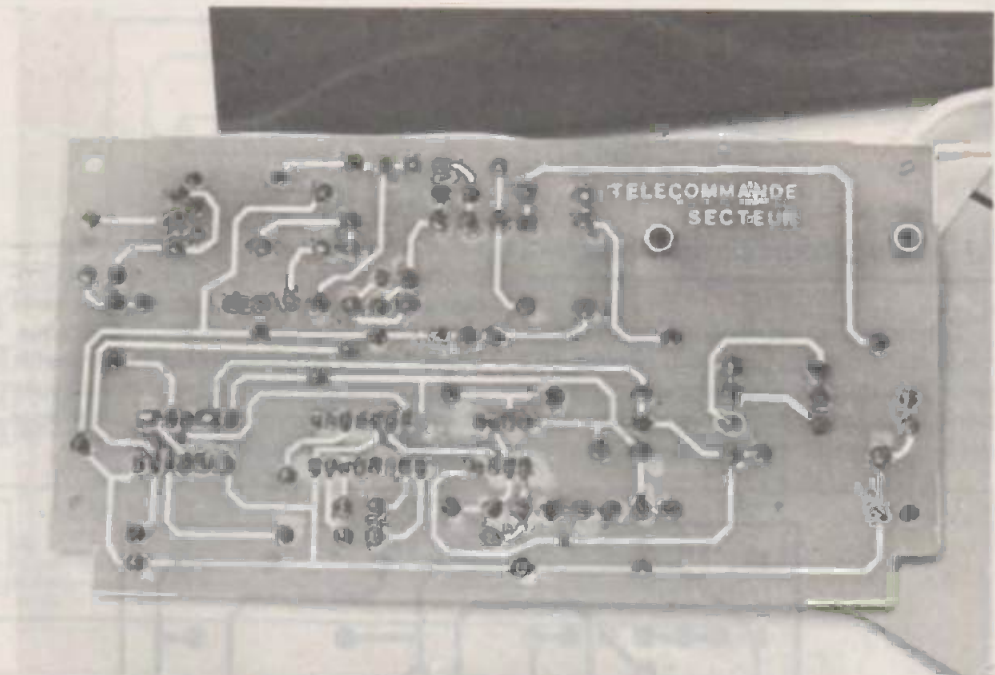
Tout le plaisir d'un tracé proprement reproduit.
